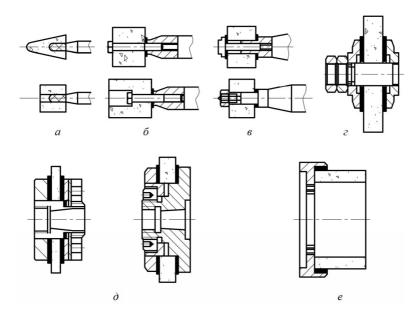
Конструкции устройств для крепления шлифовальных кругов: $a, \, \delta, \, e$ — для внутреннего шлифования; e — для круглого и плоского шлифования; e — для шлифования торцом круга
